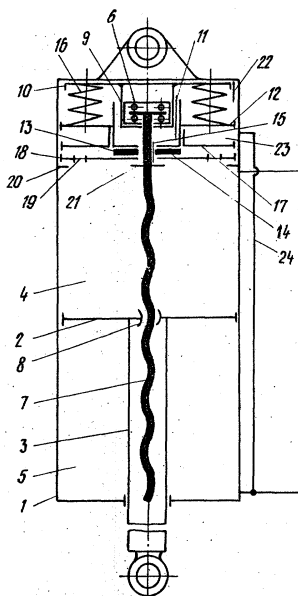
Гидравлический силовой цилиндр с механическим блокированием штока
